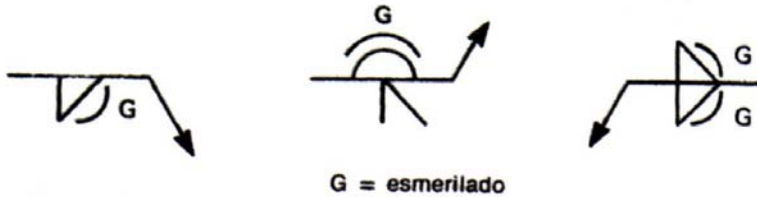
Símbolos de acabado para soldaduras convexas acabadas mecánicamente
